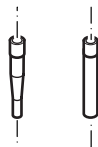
4 Einige Beispiele verschiedener Ausführungen von Schweißelementen für Short Cycle
